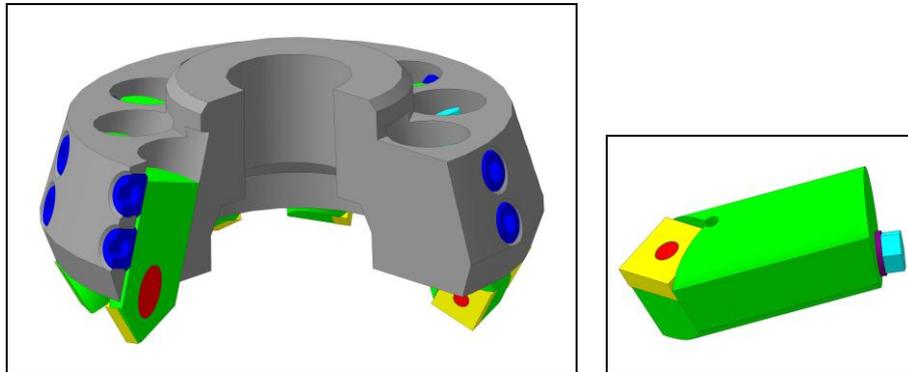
Разрез торцевой фрезы и цилиндрическая режущая вставка, содержащая четырехгранную твердосплавную пластину (3D-модели)
